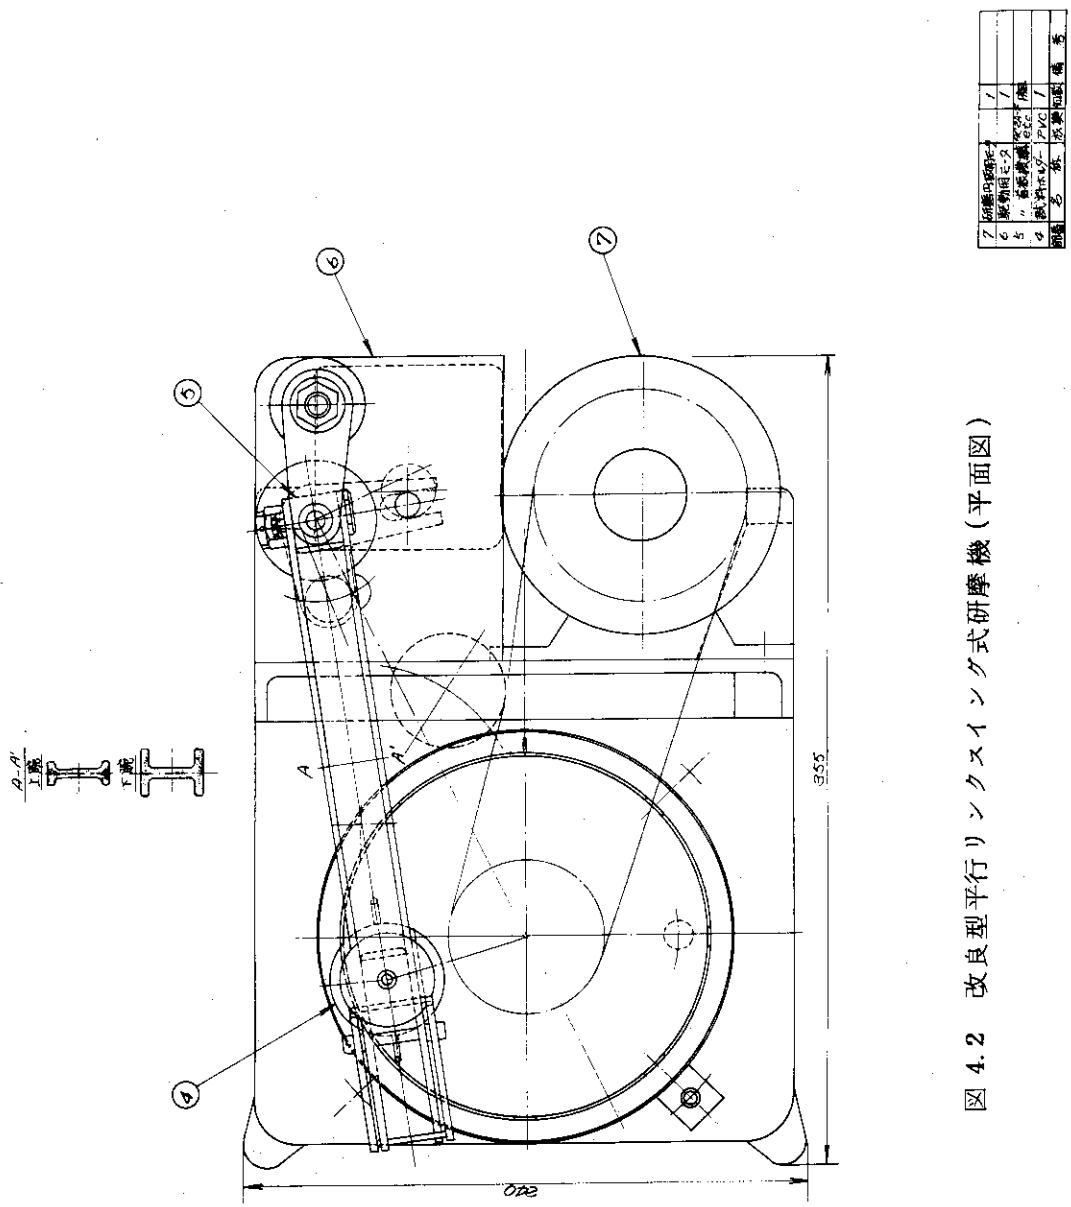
改良型平行リンクスインク式研摩機（平面図）
